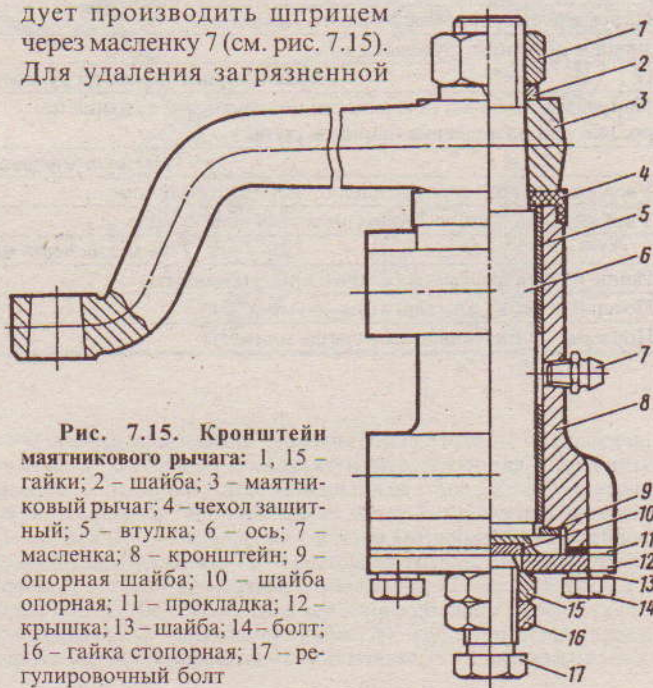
Кронштейн маятникового рычага: 1, 15 – гайки; 2 – шайба; 3 – маятниковый рычаг; 4 – чехол защитный; 5 – втулка; 6 – ось; 7 – масленка; 8 – кронштейн; 9 – опорная шайба; 10 – шайба; 11 – прокладка; 12 – крышка; 13 – шайба; 14 – болт; 16 – гайка стопорная; 17 – регулировочный болт
